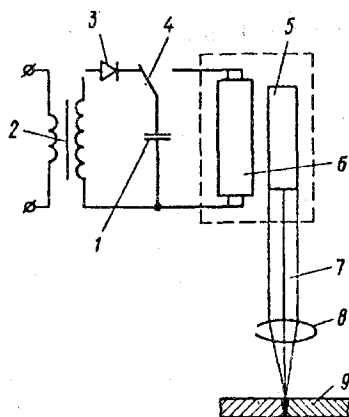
Лазерная сварка: 1 — высоковольтный конденсатор; 2 — повышающий трансформатор; 3 — выпрямитель; 4 — переключатель; 5 — рубиновый кристалл; 6 — импульсная лампа; 7 — луч лазера; 8 — оптическая система; 9 — свариваемое изделие
